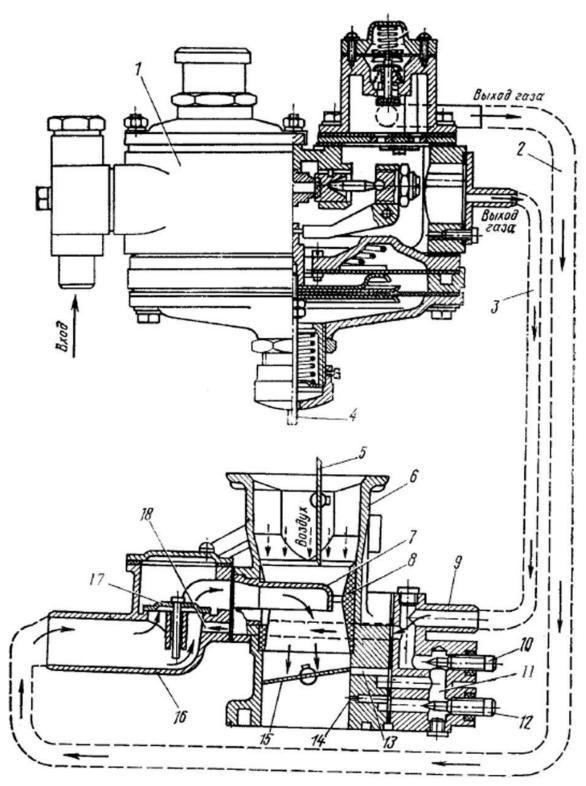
Схема газового смесителя и его соединения с газовым редуктором: 1-корпус газового редуктора; 2 - шланг подвода газа к главной дозирующей системе смесителя; 3 - трубка подвода газа к системе холостого хода смесителя; 4 - стержень диафрагмы второй ступени редуктора; 5 - воздушная заслонка; 6- корпус смесителя; 7 - газовая форсунка; 8 — диффузор; 9 - крышка с патрубком подвода газа и каналами системы холостого хода смесителя; 10, 12 - винты регулировки работы смесителя при холостомходе; 11,18 — каналы; 13, 14 - отверстия для
